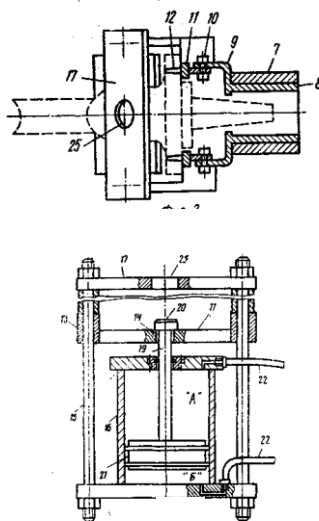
Фиксатор с кронштейном и втулкой, вид сверху и - рамка с механизмом для выпрессовки в разрезе.
